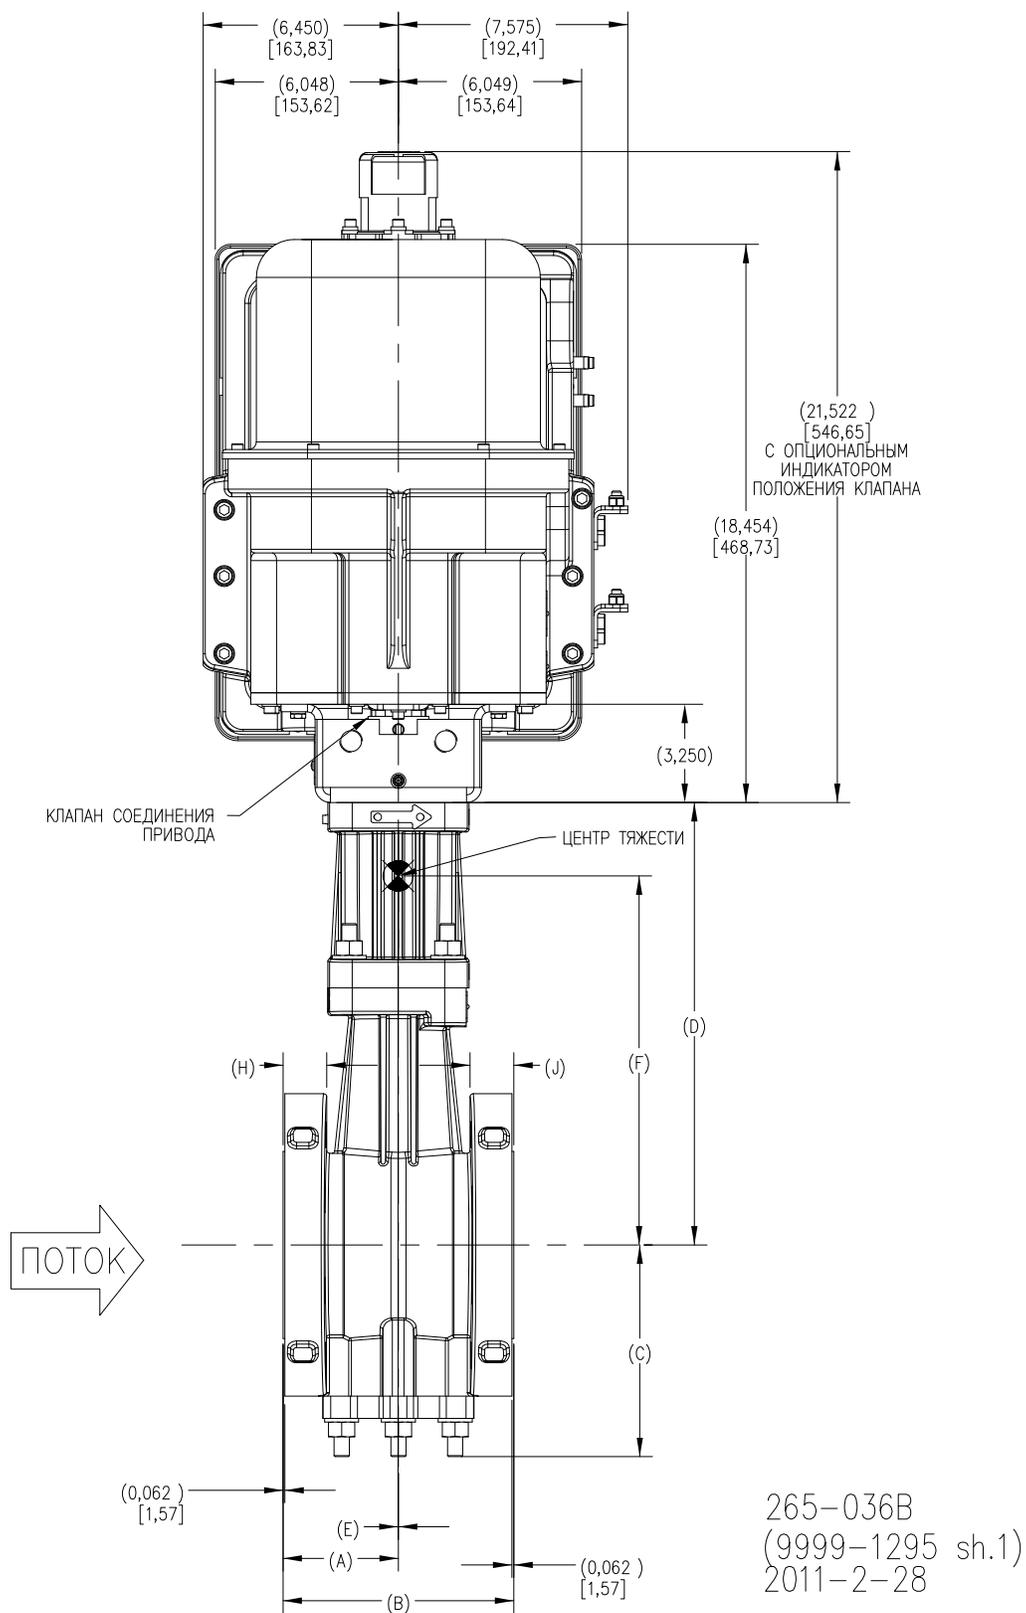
Габаритно-присоединительный чертеж RVP-200
